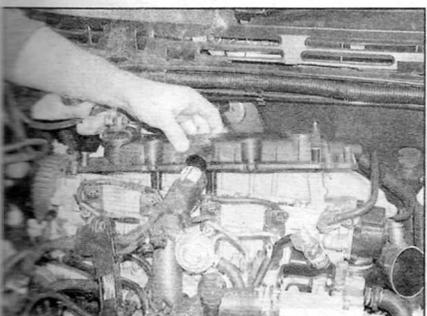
Снятие крышки головки цилиндров (двигатели 2.0 л)
